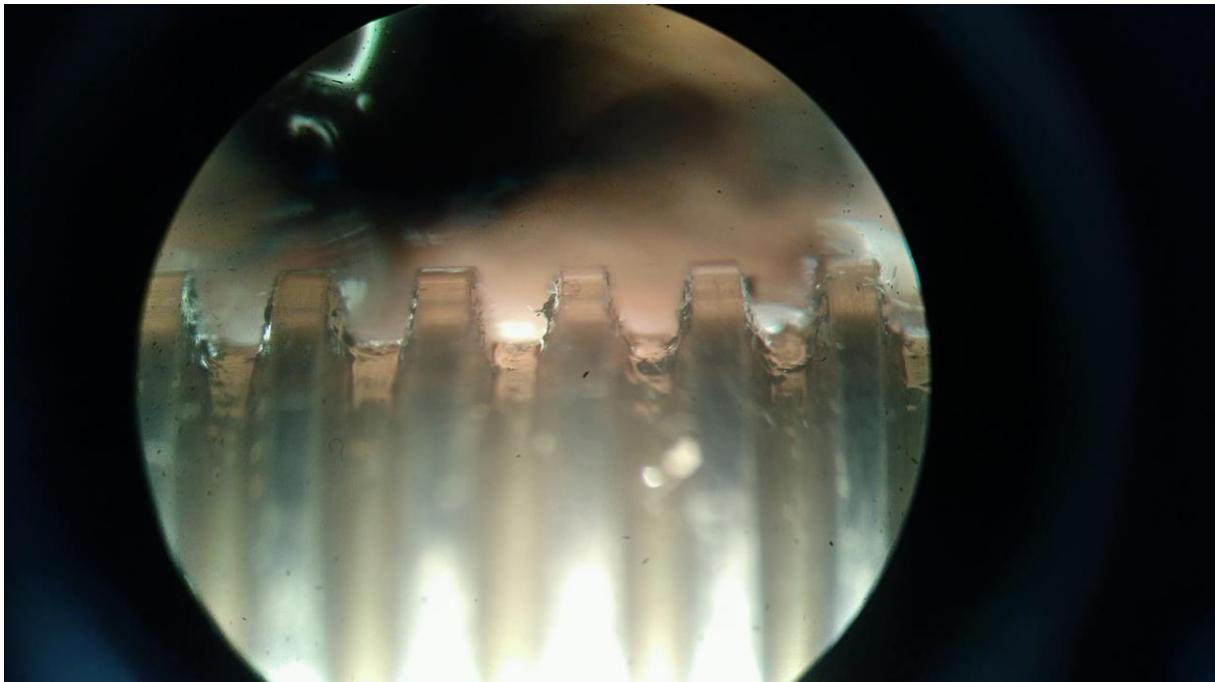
Mikroskopaufnahme des Gewindes der Z-Spindelmutter
